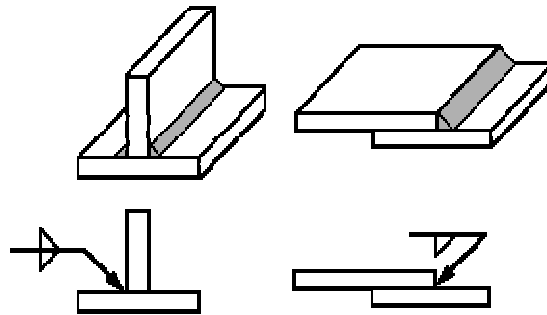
Aplicación de símbolos de soldadura de filete.
